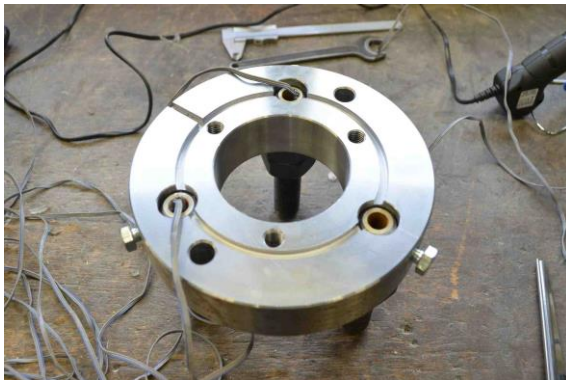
Kopfteil mit gefrästen Kabelkanälen, DMS zentrisch in Gewindestangen (M20, FK10.9) eingeklebt
